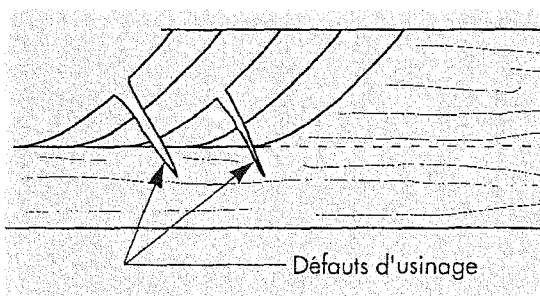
Défauts d'usinage dus à la coupe par fendage (d'après Koch, 1964)
